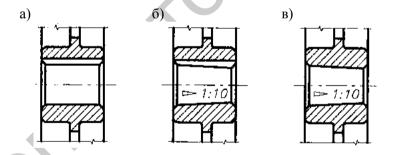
Посадочные отверстия шкивов: а) цилиндрическое со шпонкой; б) коническое со шпонкой; в) коническое
